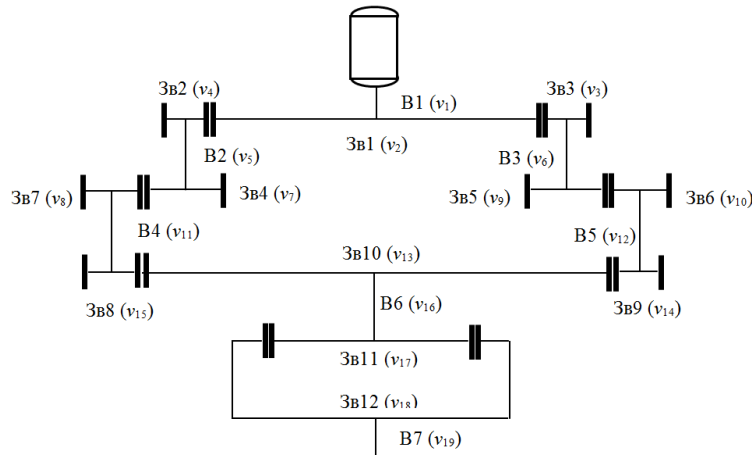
Схема кинематической цепи редуктора ЭМП, где Зв – звено, В – вал
